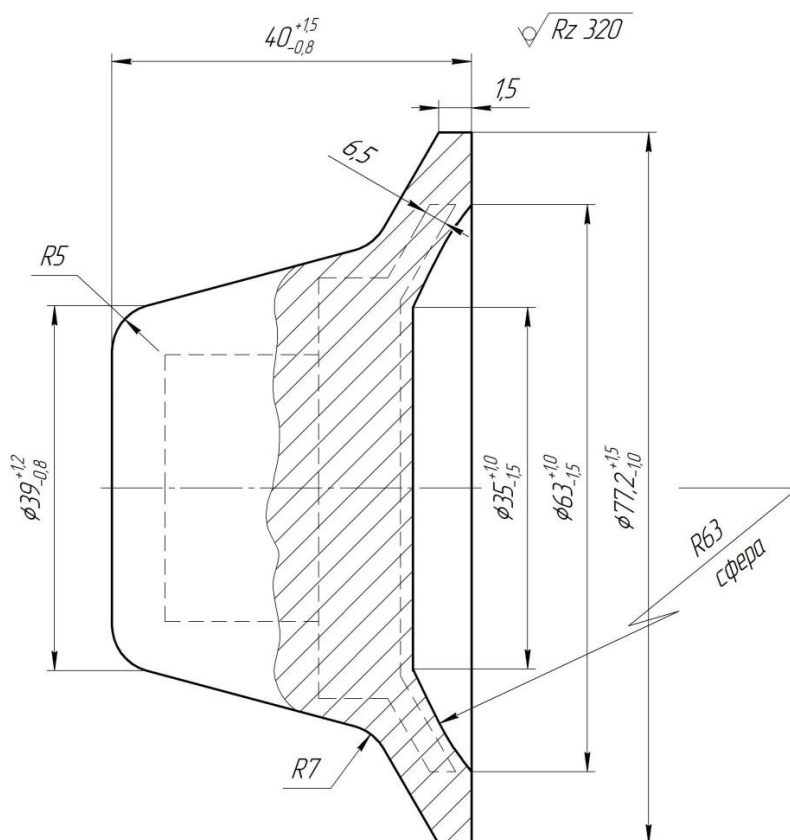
Эскиз заготовки детали «Стакан», полученной методом горячей штамповки
